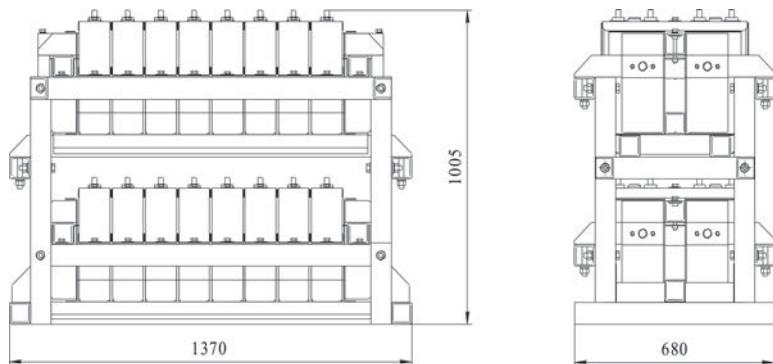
Габаритный чертеж СА-У1
